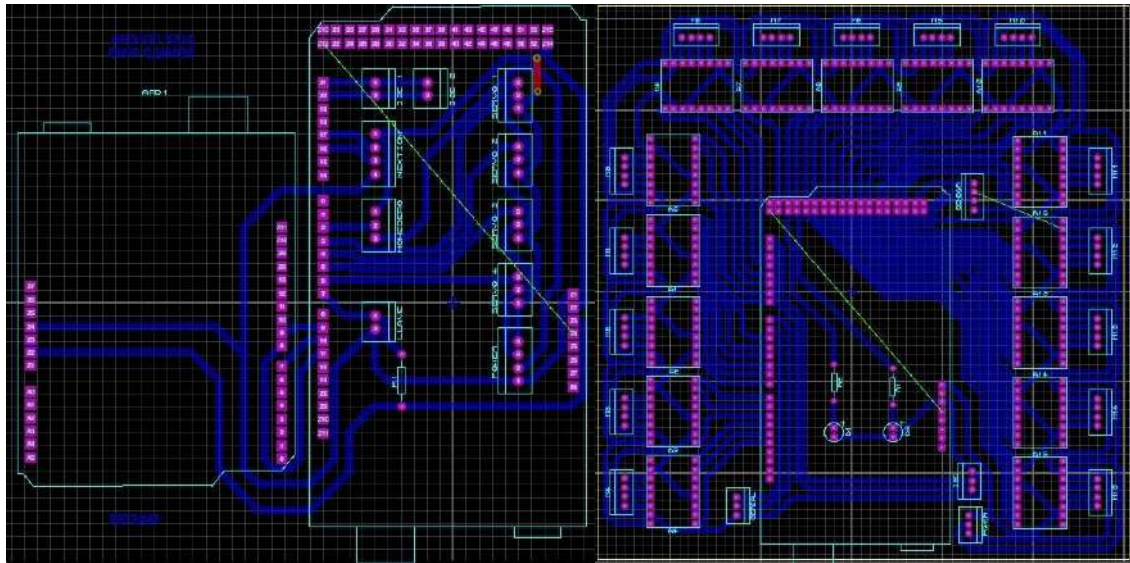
Diseño de PCB para la placa del maestro y los esclavos
